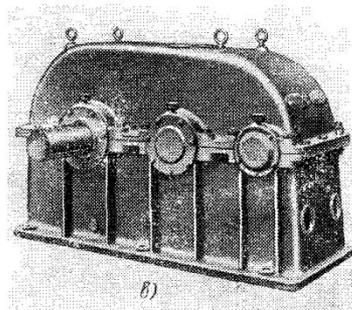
Разновидности двухступенчатых редукторов с цилиндрическими зубчатыми колесами
